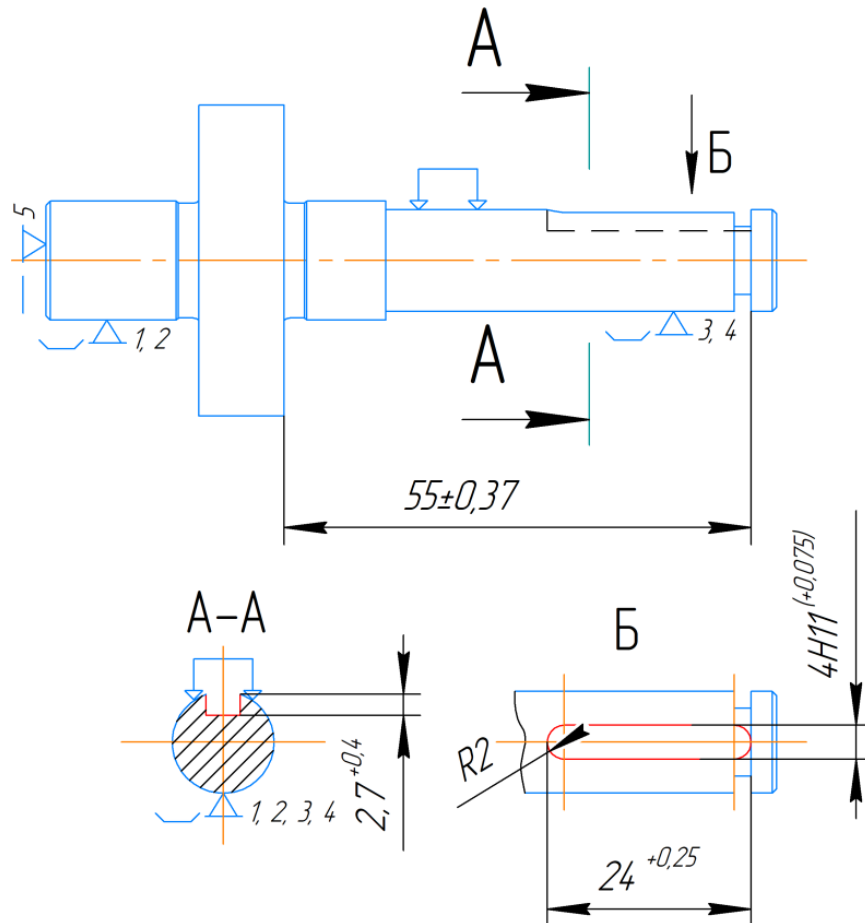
Схема базування заготовки 025 за схемою №2
